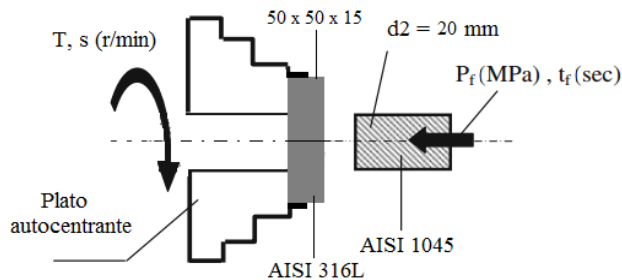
Modelo para cálculo de la soldadura por fricción. Fuente: Mumin *et al.* (2017).
